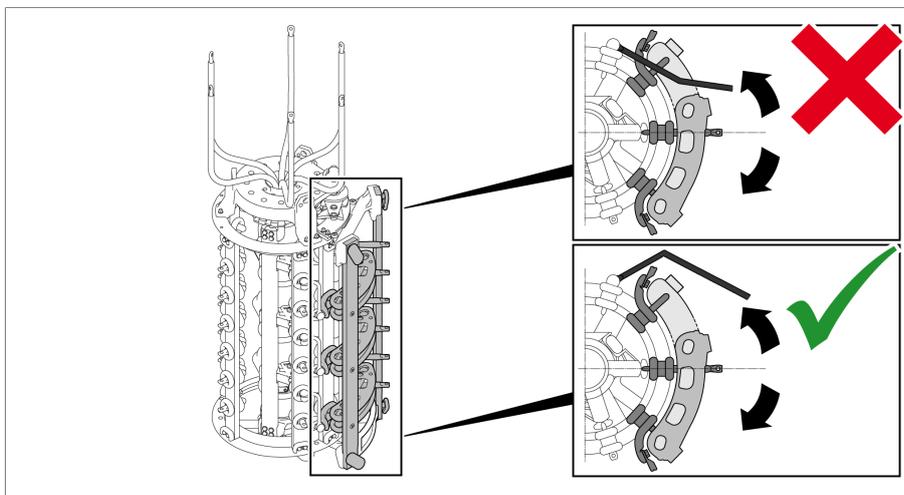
Присоединительные контакты предизбирателя при переключении с реверсом (вид сверху)
